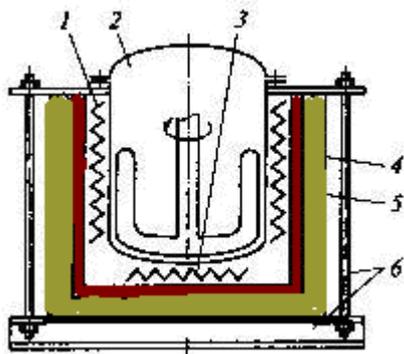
Электрическая печь сопротивления: вертикальная секция; 2 – котел; 3 – донная секция; 4 – огнеупорная кладка; 5 – тепловая изоляция; 6 – опускное устройство печи
